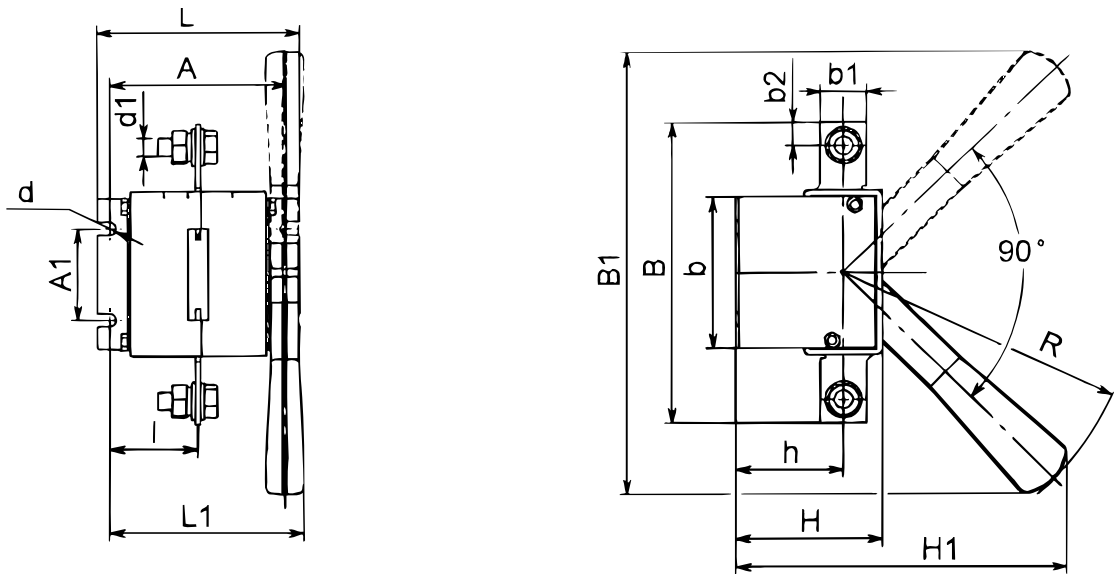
Выключатель-разъединитель однополюсный на одно направление с боковой рукояткой
